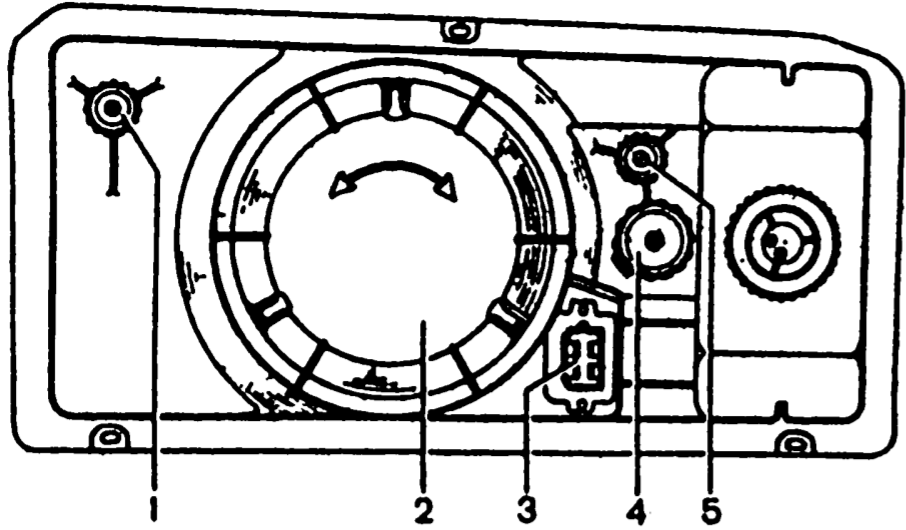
Вид на блок-фару из отсека двигателя: 1 - винт регулировки пучка света в горизонтальном направлении; 2 - кожух фары; 3 - штепсельная колодка; 4 - установочный винт; 5 - винт регулировки пучка света в вертикальном направлении
